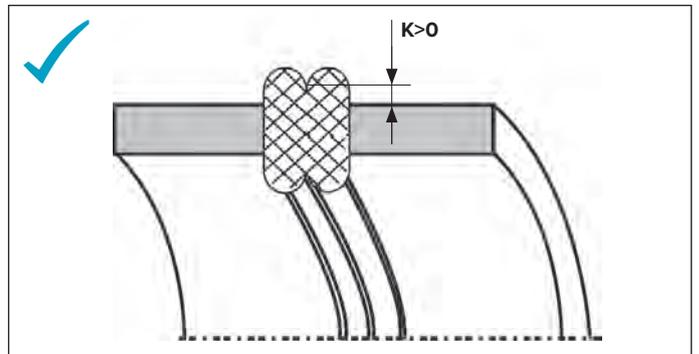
Sección transversal de un buen cordón de soldadura.
